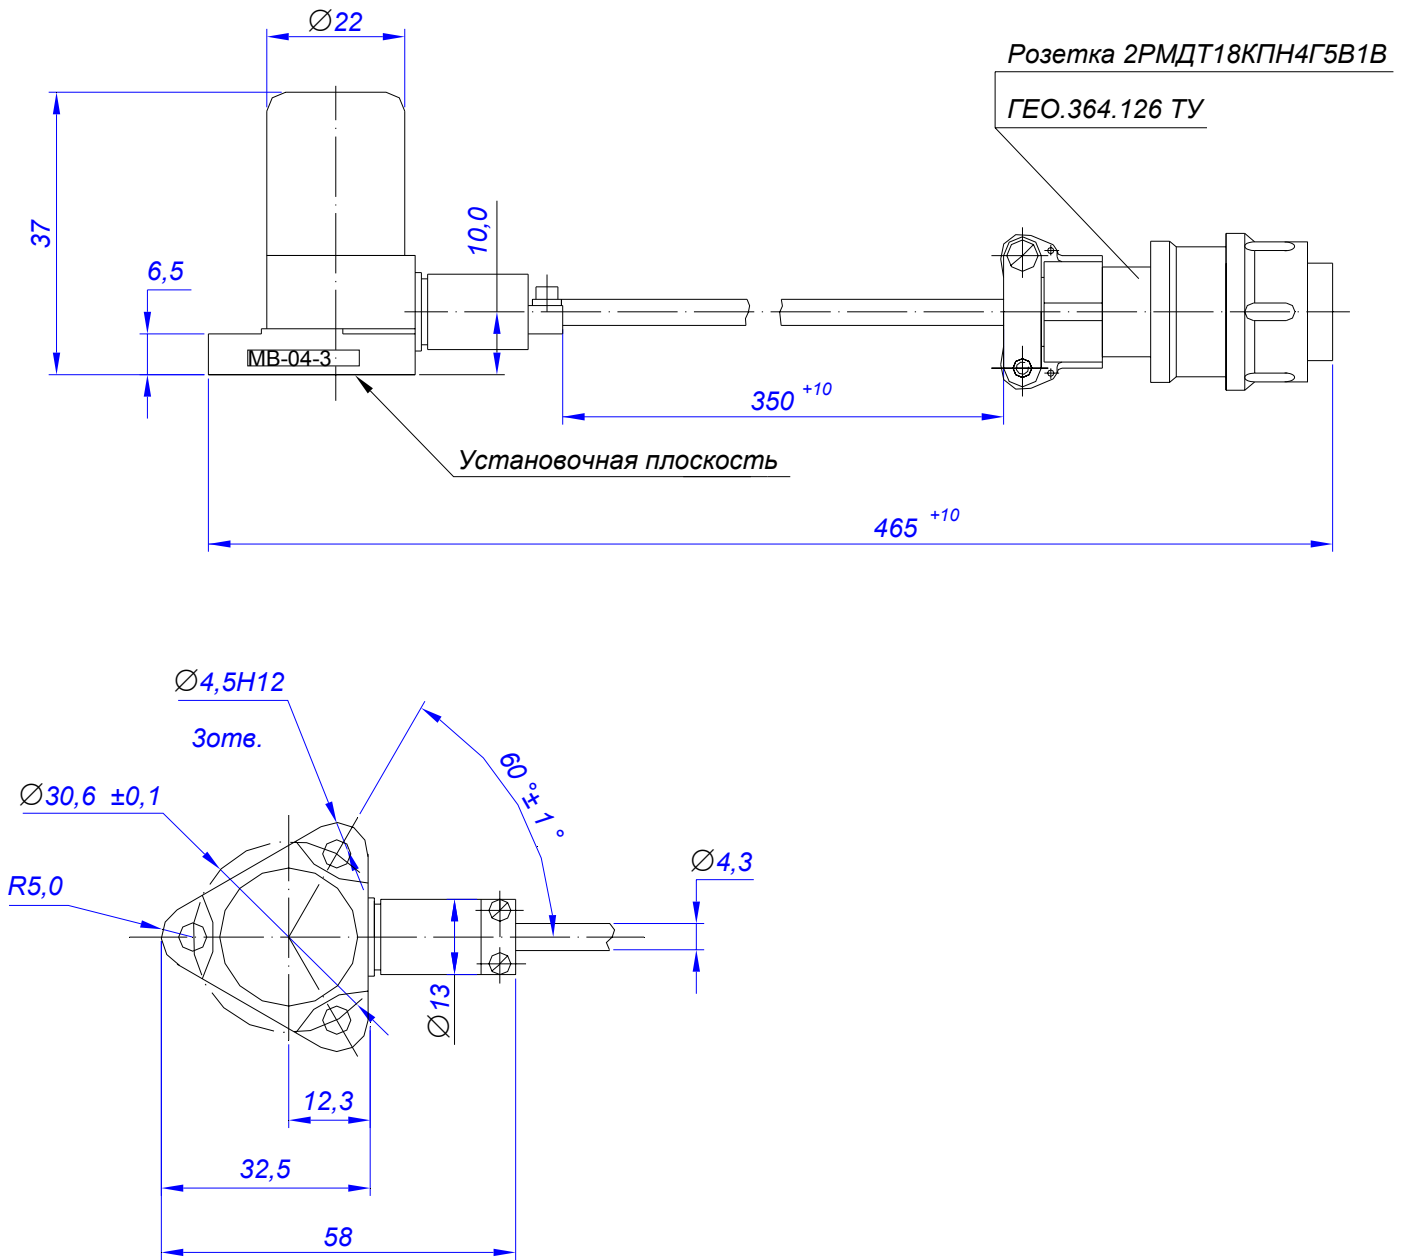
Габаритно-установочные размеры датчика вибрации MB-04-3
